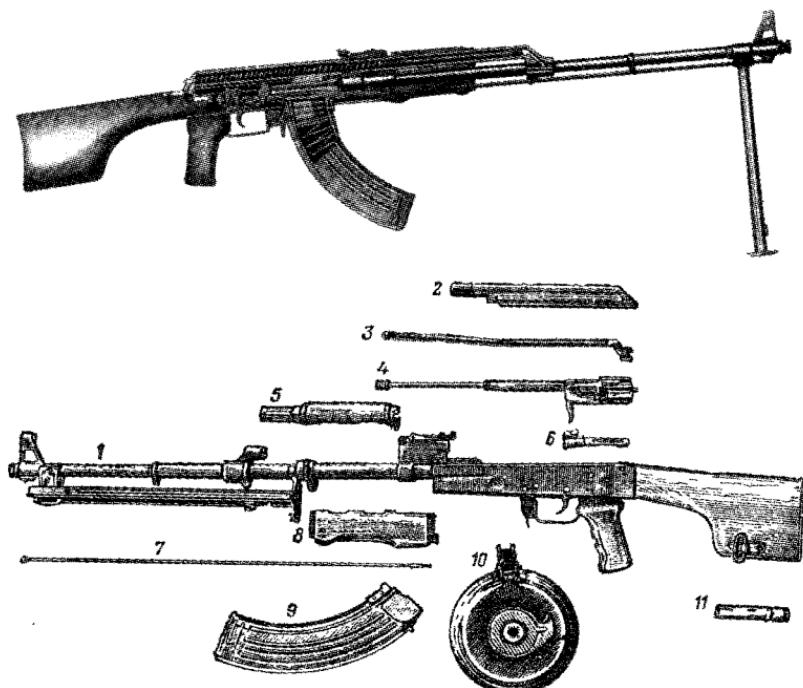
Базовая модель карабинов серии «Вепрь» – 7,62 мм ручной пулемет Калашникова РПК: 1 – общий вид; 2 – устройство; 3 – основные части и механизмы: 1 – ствол со ствольной коробкой, прицельным приспособлением, сошкой и прикладом; 2 – крышка ствольной коробки; 3 – возвратный механизм; 4 – затворная рама с газовым поршнем; 5 – газовая трубка со ствольной накладкой; 6 – затвор; 7 – шомпол; 8 – цевье; 9 – коробчатый магазин; 10 – барабанный магазин; 11 – коробка с принадлежностью.
